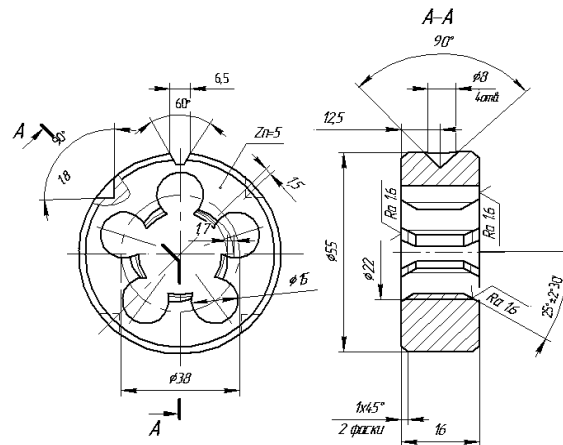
Плашка різьбонарізна (креслення)
